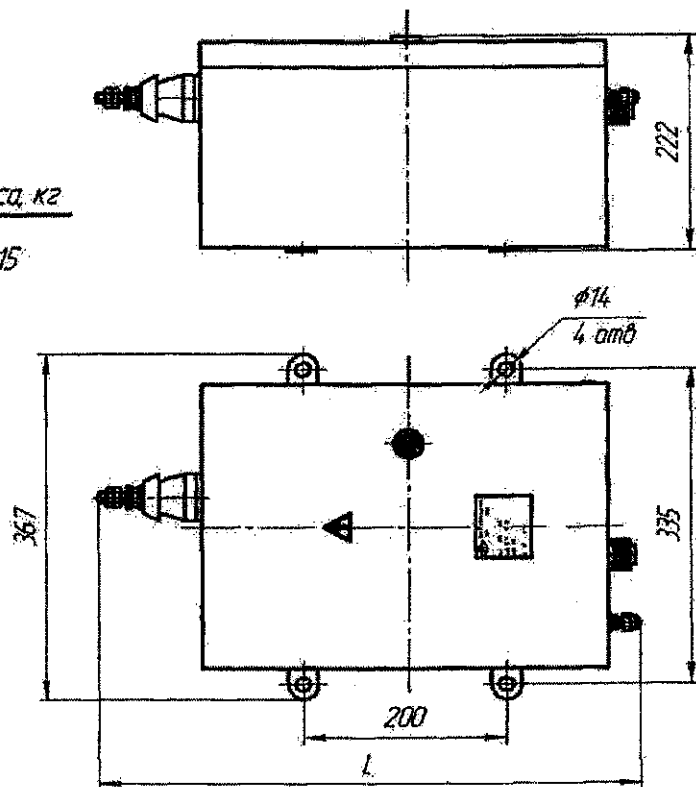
Габаритные размеры фильтра присоединения типа ФПЭ
